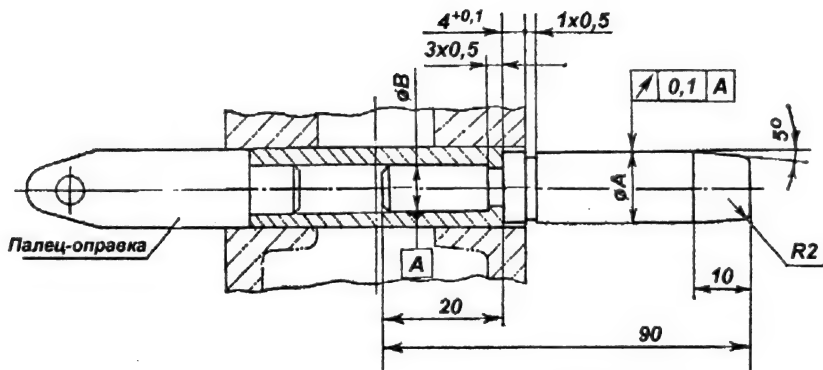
Оправка для запрессовки и выпрессовки поршневого пальца
